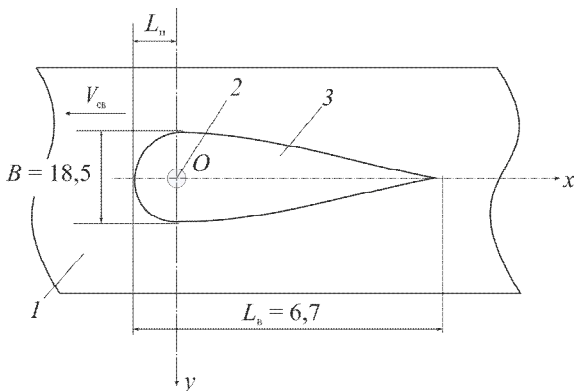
Вид сверху на модель сварочной ванны
